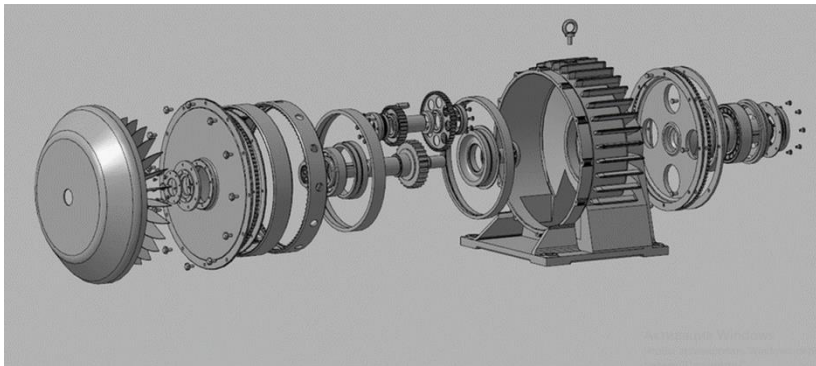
Трехмерная модель разнесенной сборки редуктора
